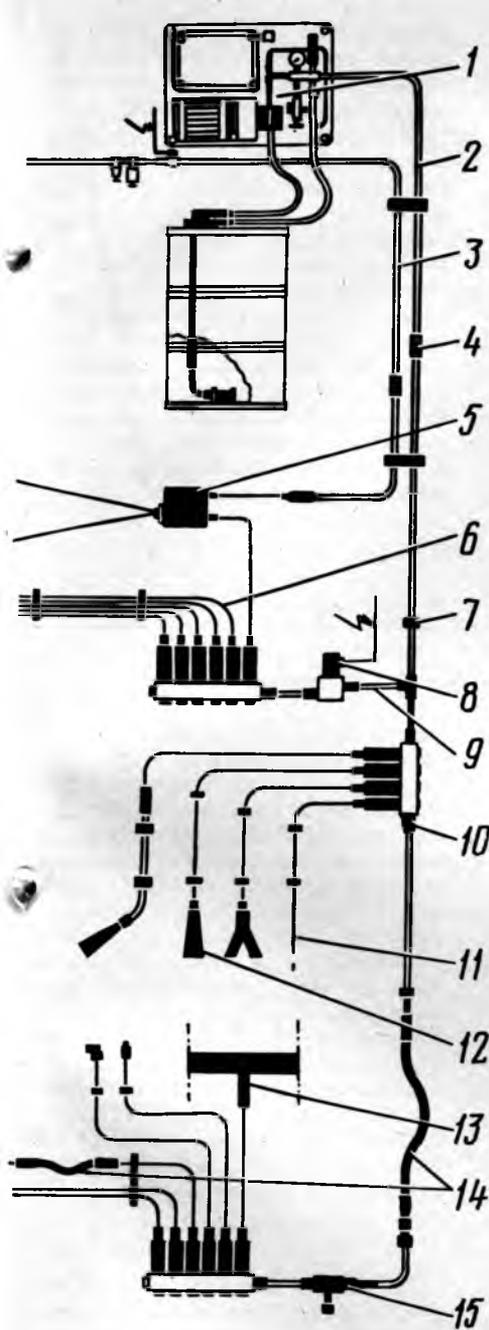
Стационарная установка для смазки трущихся поверхностей деталей поточных линий:
